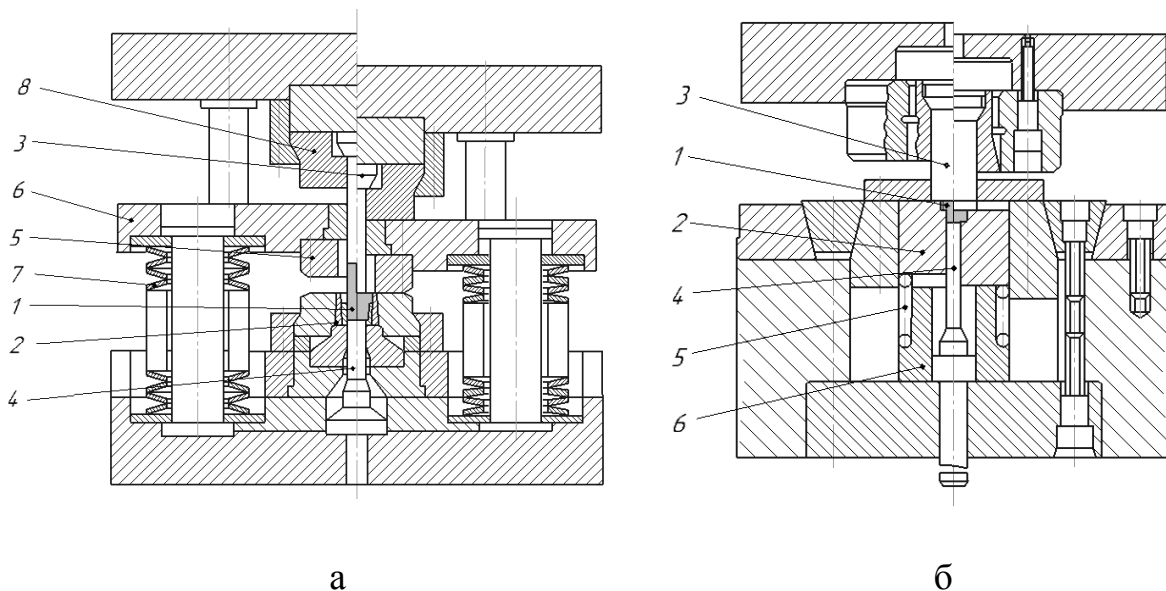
Варіанти конструкцій штампів для калібрування різних заготовок способом радіального видавлювання
